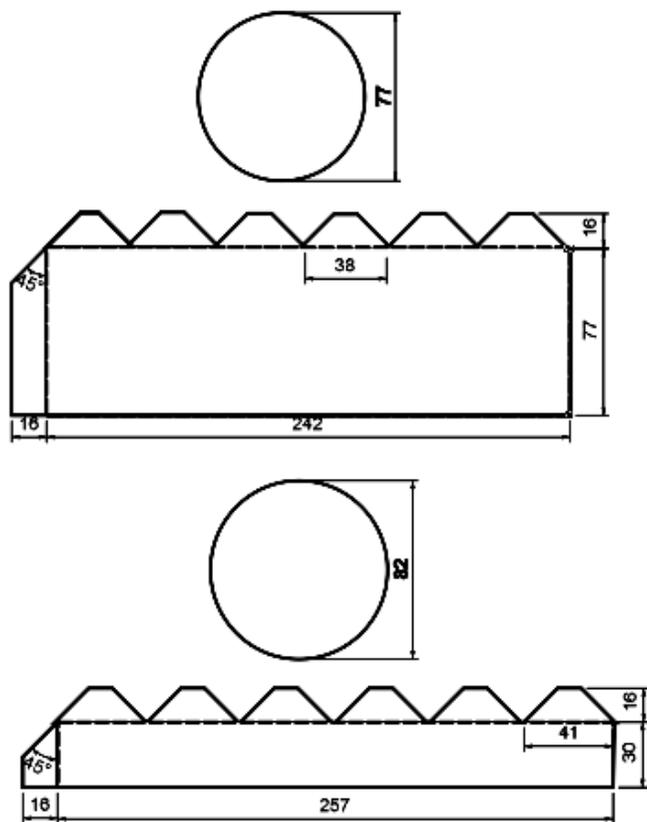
Развертка упаковки с цилиндрическим основанием.
